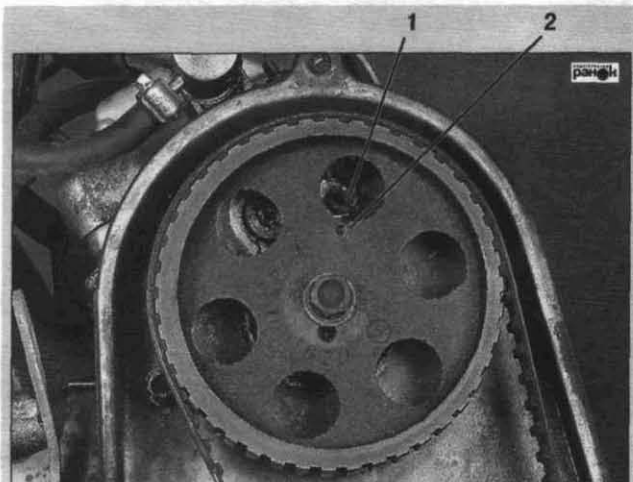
Установочные метки на шкиве распредвала: 1 — установочный болт; 2 — метка (сверление)
